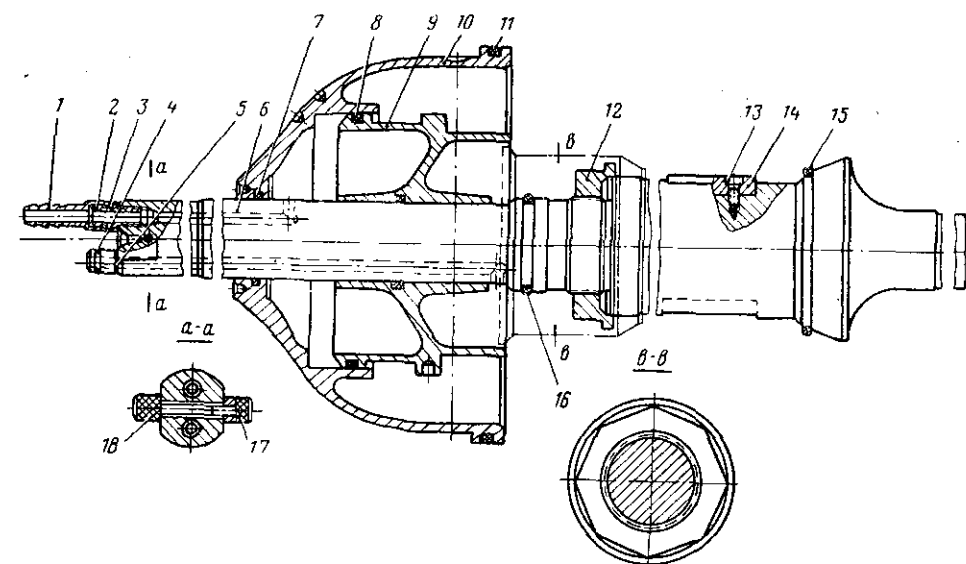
Эквипираторный вал 63689/464 для балансировки винта:
